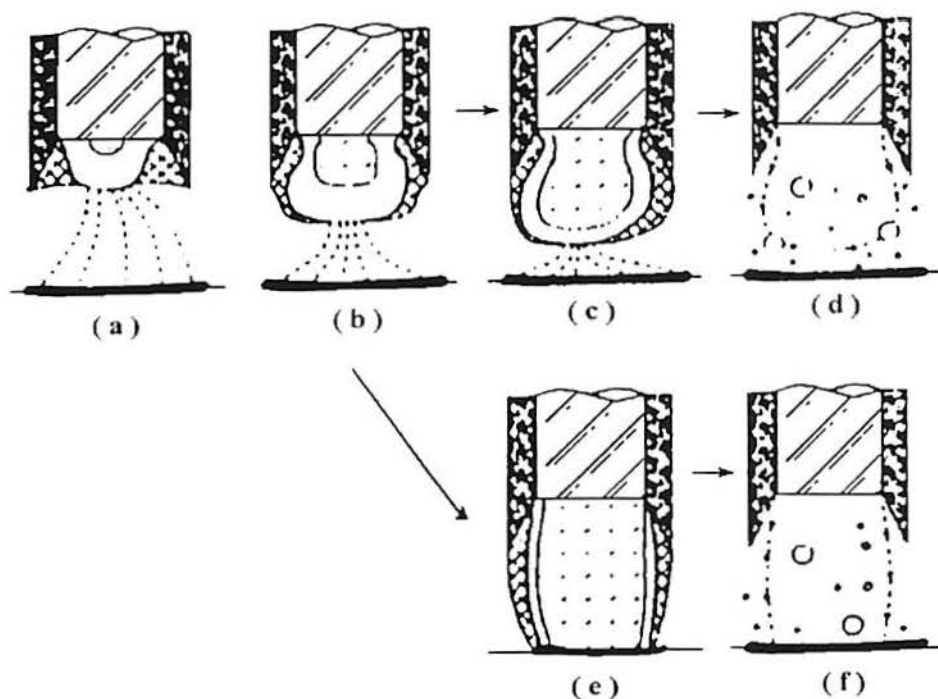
Mecanismo de transferência do metal de solda proposto por Larson, [44].
